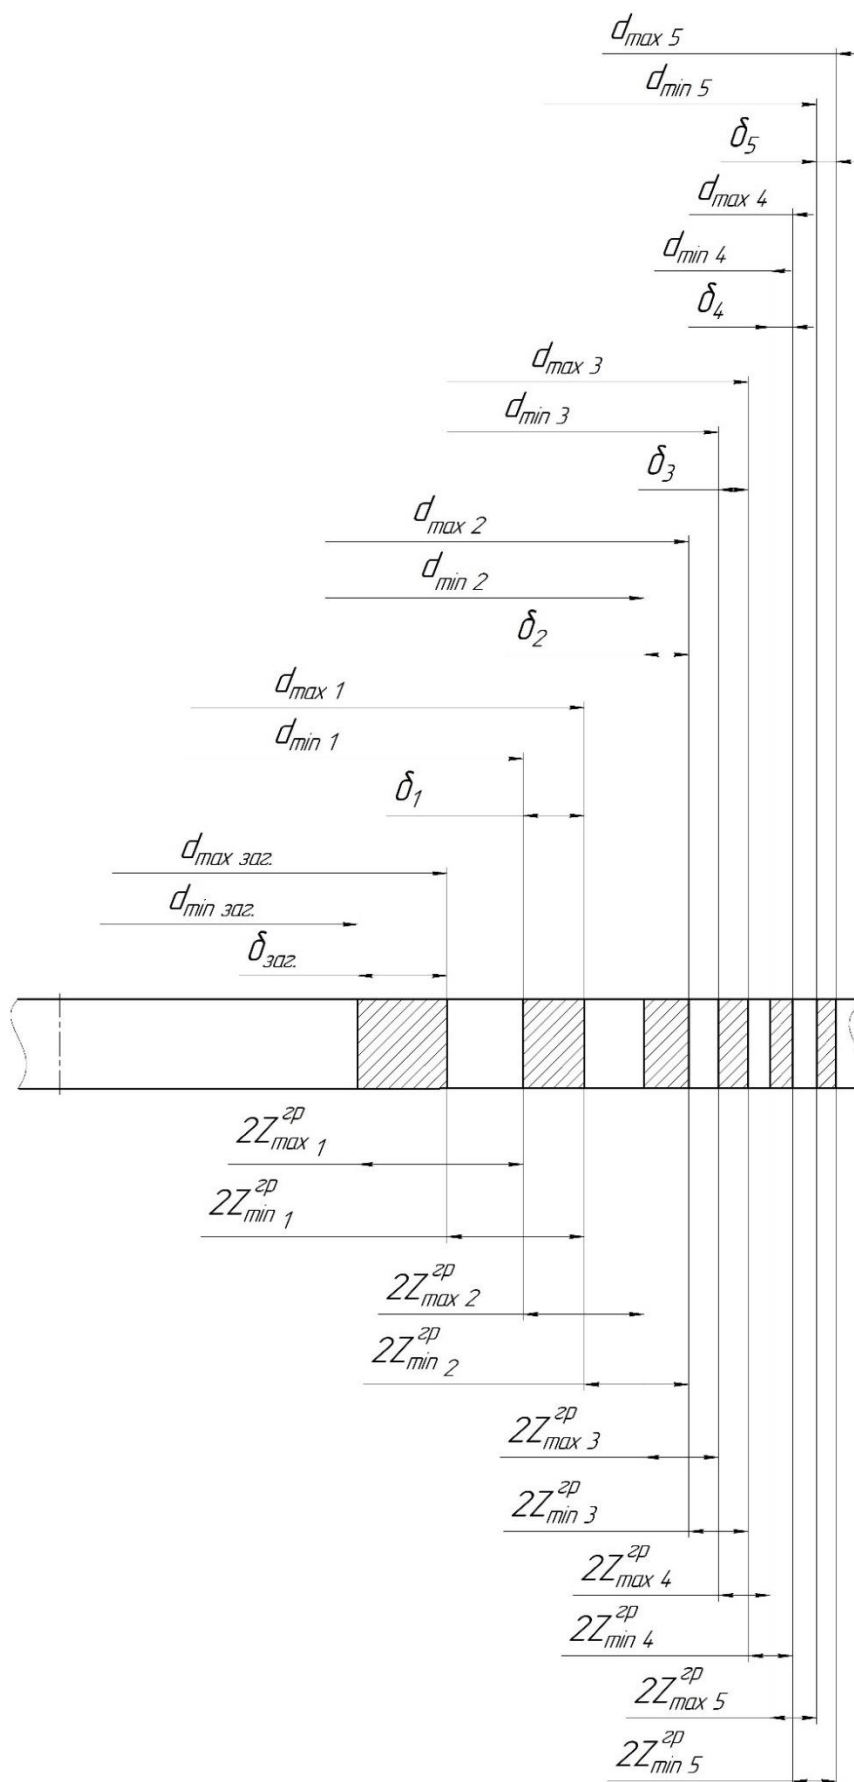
Схема графічного розташування припусків внутрішньої циліндричних поверхні
